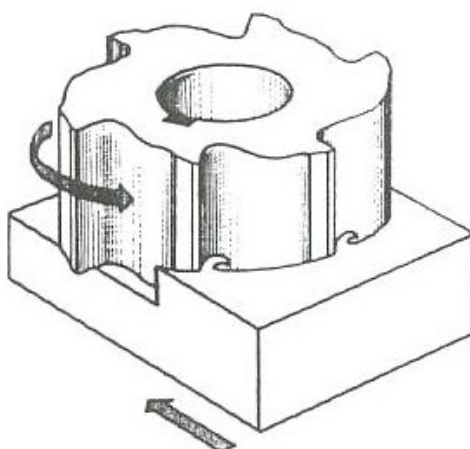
Silové poměry při sousledném frézování [1]
